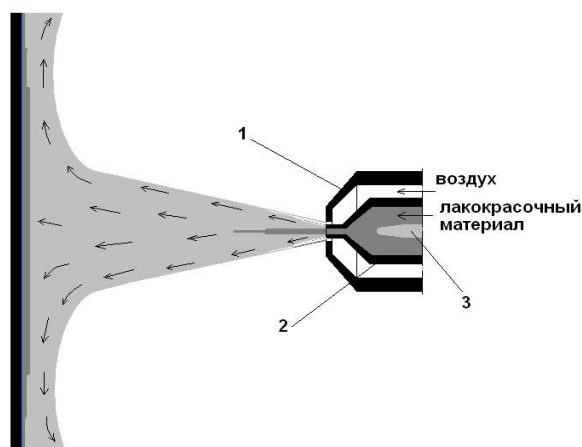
Схема дробления лакокрасочного материала методом пневматического распыления:
